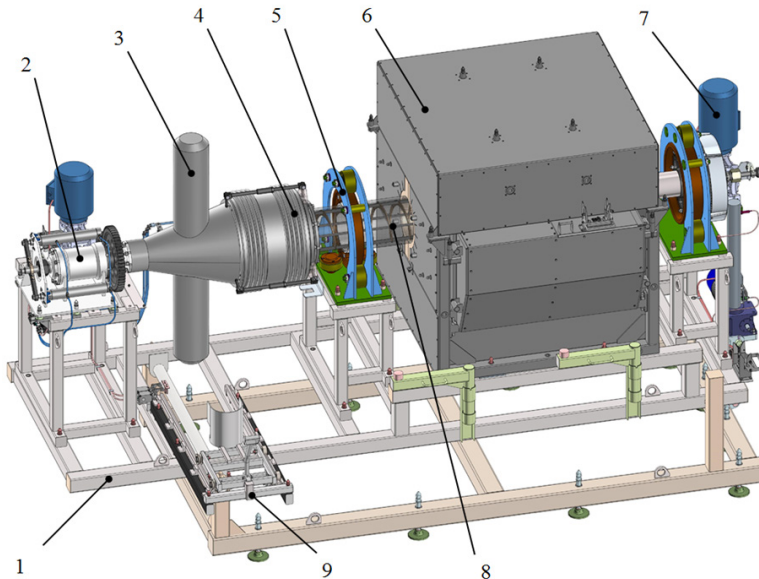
Макет установки ВТО: 1 – рама; 2 – привод камеры загрузочной; 3 – контейнер; 4 – узел уплотнения; 5 – опора реторты; 6 – камера нагревательная; 7 – привод реторты; 8 – реторта; 9 – тележка
